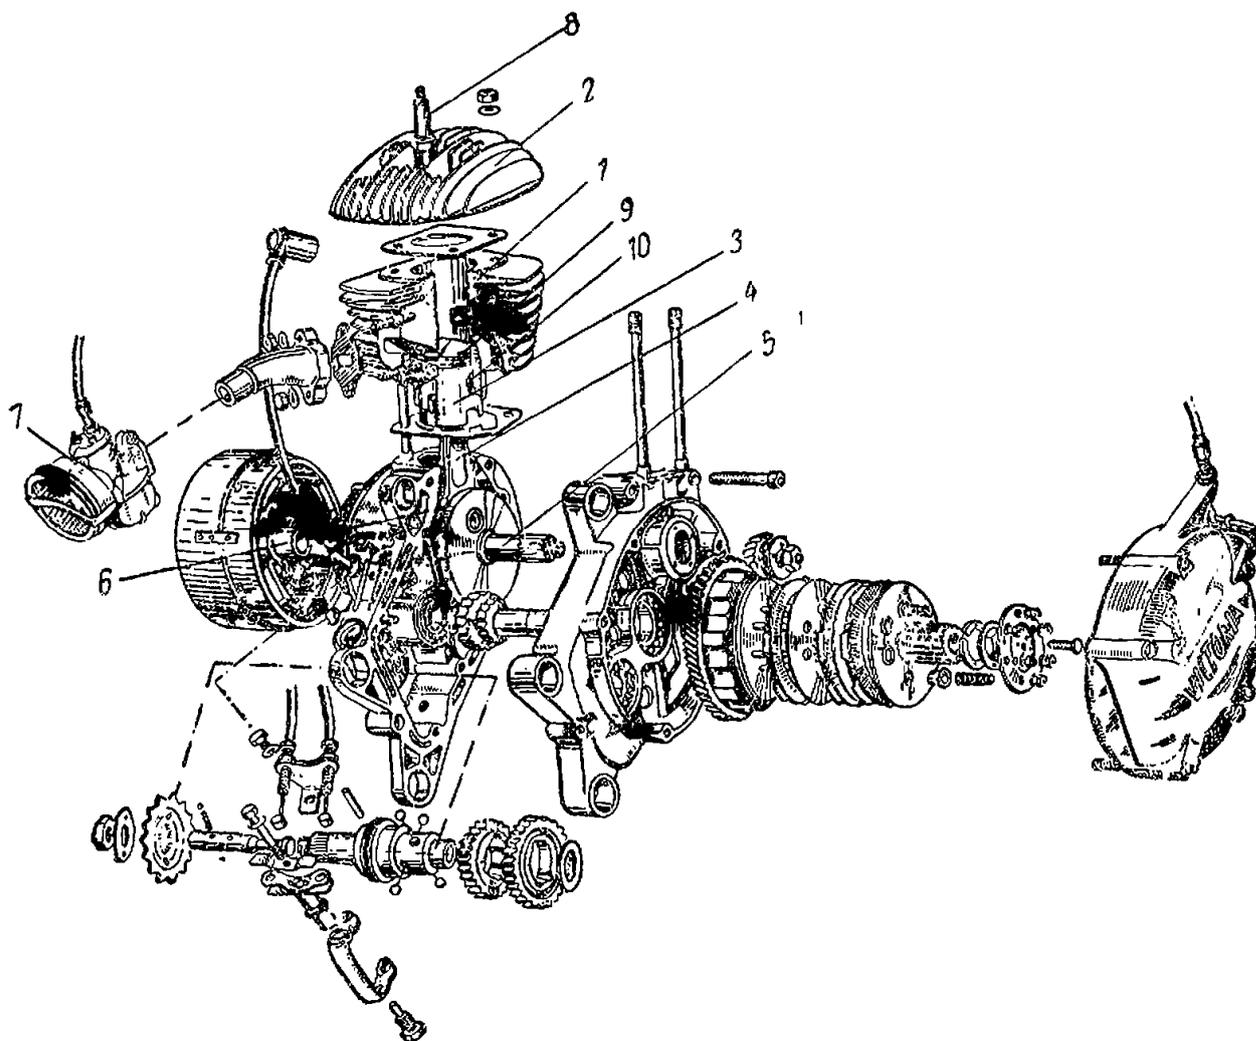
Двухтактный мотор современного мотороллера в разрезе: 1 — цилиндр; 2 — головка цилиндра; 3 — поршень; 4 — шатун; 5 — коленчатый вал; 6 — картер; 7 — карбюратор; 8 — свеча. 9 — кольца цилиндра; 10 — палец.
